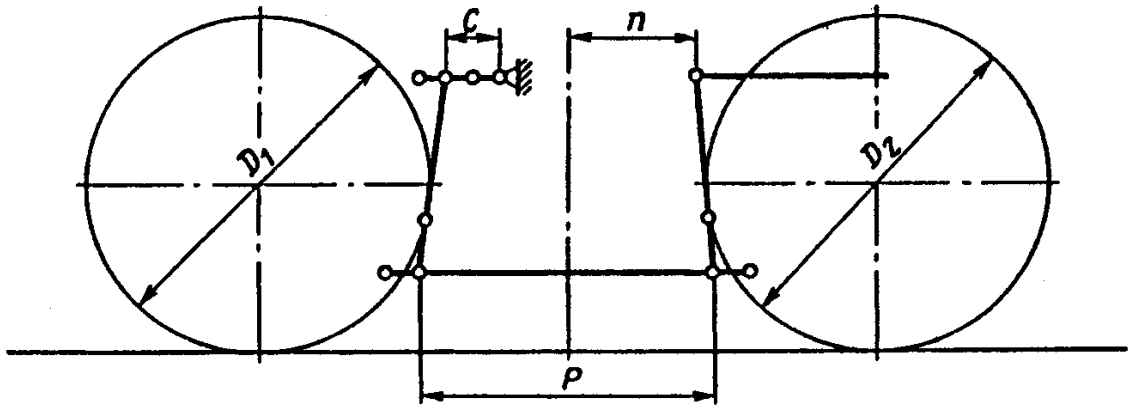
Схема тормозной рычажной передачи двухосной тележки грузового вагона
